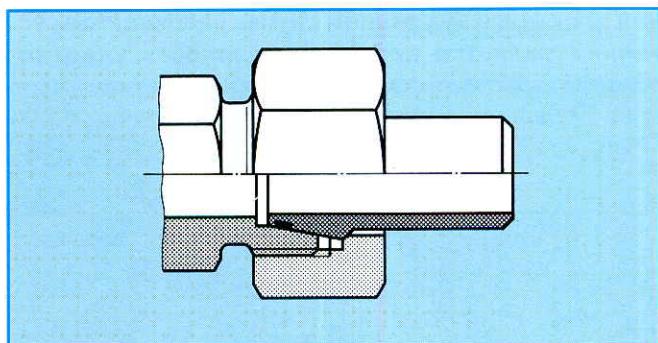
Резьбовое соединение с коническим штуцером под сварку с конусом по DIN 3865. Уплотнение: эластичное. Фиксация обеспечивается за счёт сварного шва.
